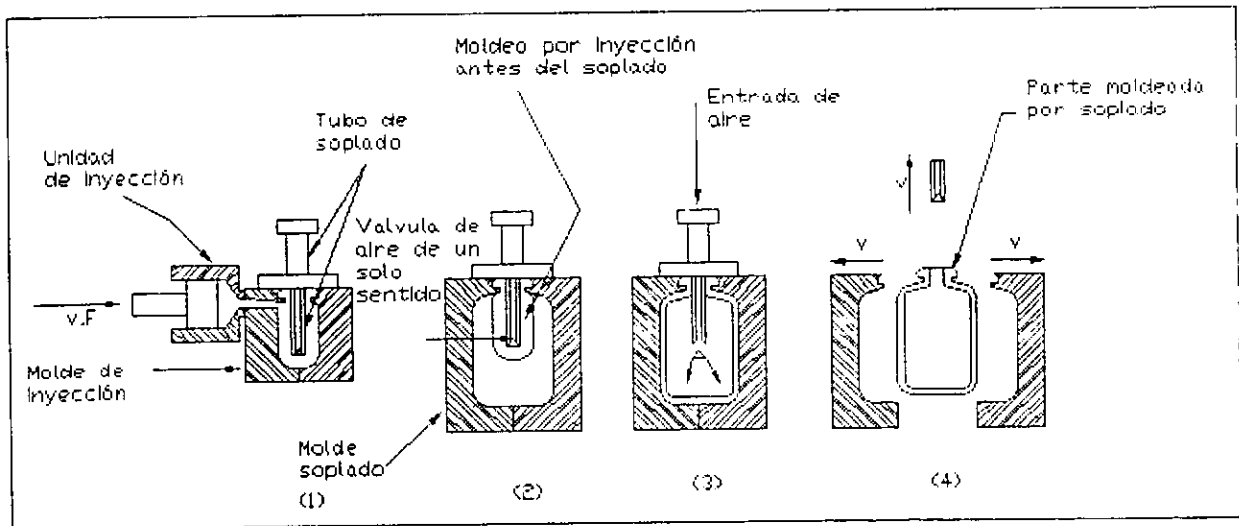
Moldeo por inyección soplado: (1) la preforma se moldea por inyección alrededor de un tubo de soplado; (2) se abre el molde de inyección y la preforma se transfiere a un molde de soplado; (3) el polímero suave se infla para que tome la forma del molde de soplado y (4) se abre el molde y se retira la pieza.¹⁵
